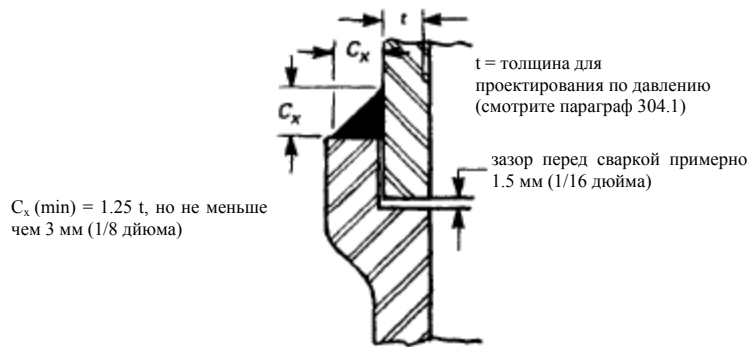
С. Минимальные сварочные размеры для компонентов, сваренных муфтовым способом, отличных от фланцев.
